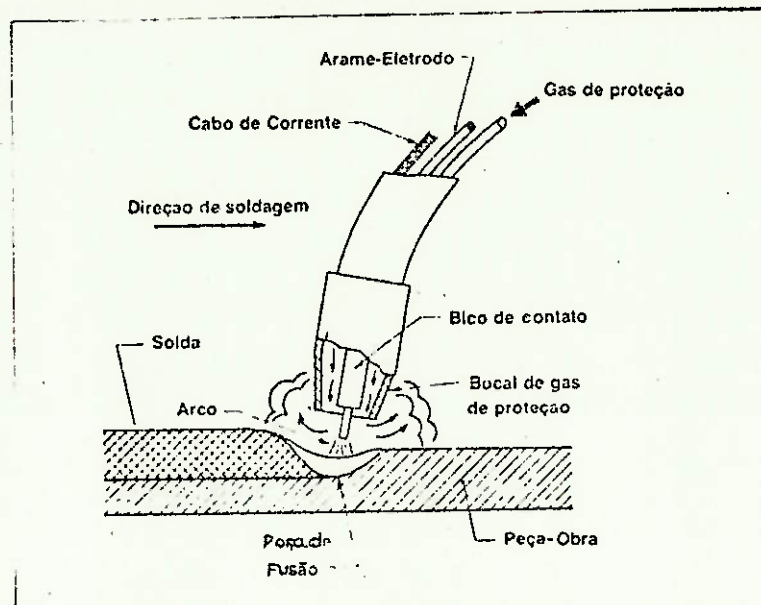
REPRESENTAÇÃO ESQUEMÁTICA DO EXTREMO DE UMA PISTOLA DE SOLDAGEM MIG/MAG
